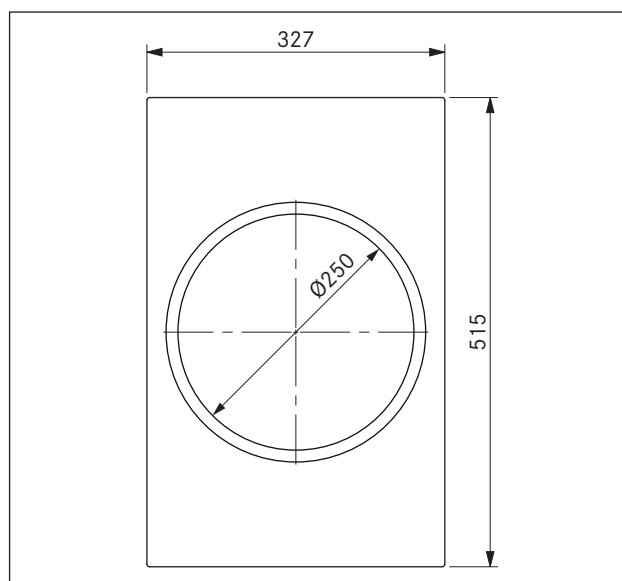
Dimensões do aparelho CKIW, vista de cima
